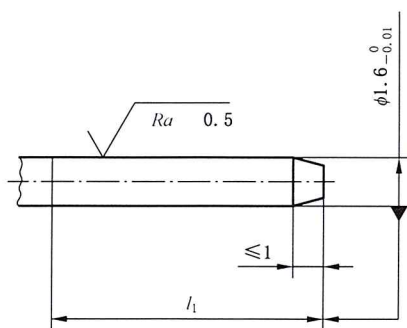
3 型杆的尺寸、公差和表面粗糙度
